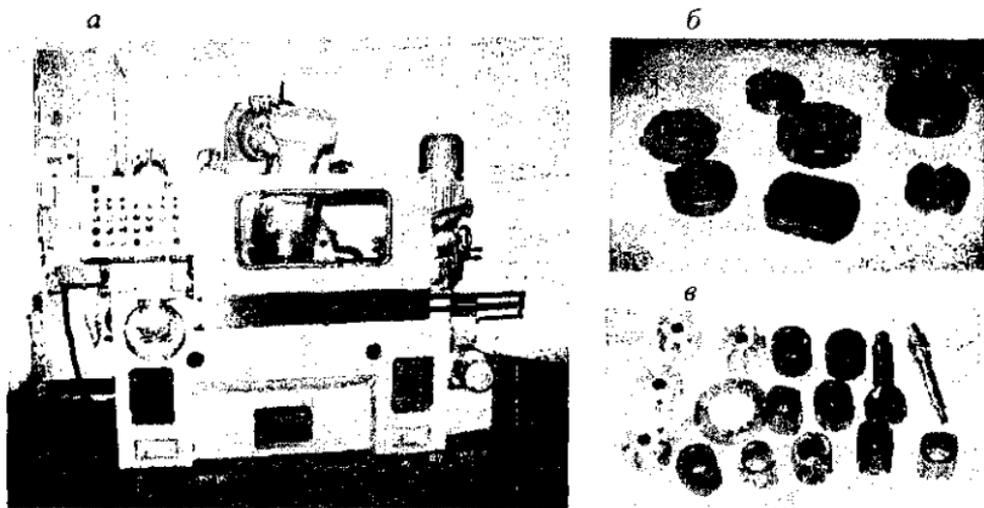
Станок модели ВС-50: а – общий вид станка; б – специальные инструменты для обработки профильных и прерывистых поверхностей; в – образцы деталей, обработанных на станке
